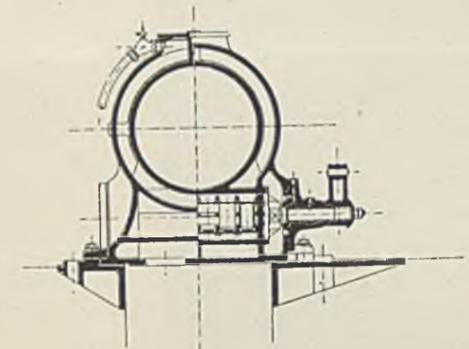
Schnitt durch den Niederdruck-Lufteylinder des liegenden Stufen-Kompressors von Th. Calow & Co., Bielefeld.
